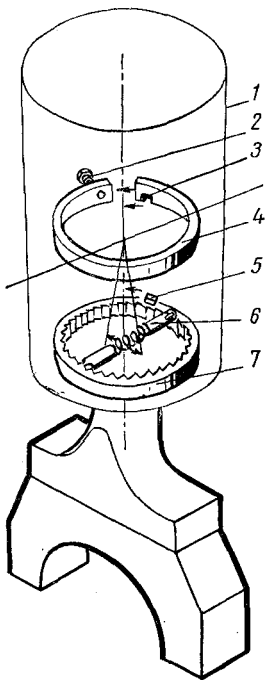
Эскиз механизма поворота поршня двигателя Зульцер:
